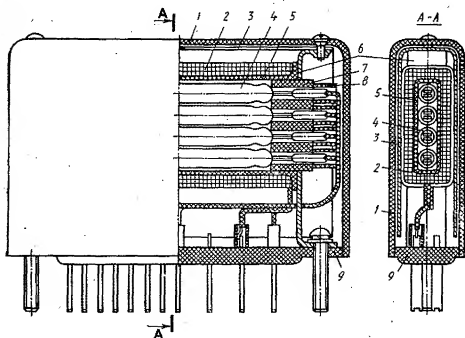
Конструкция многоконтактного реле типа РПГ на герконах нормального типоразмера для систем промышленной автоматики: 1 — пластмассовый кожух; 2 — обмотка; 3 — ферромагнитный экран; 4 — геркон; 5 — каркас катушки; 6 — скоба; 7 — пластмассовые колодки; 8 — резиновые трубки; 9 — основание
